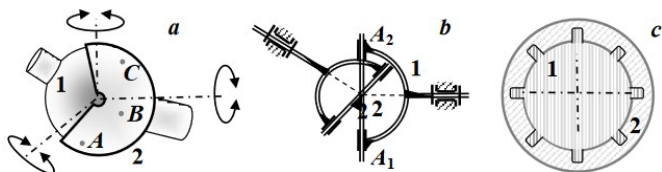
Кинематические пары с элементарными (а) и разделительными (b, c) избыточными связями
